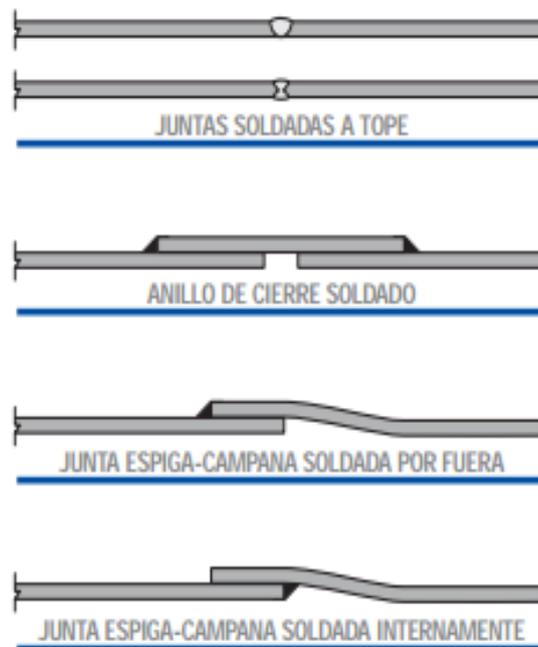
Juntas por soldadura en tuberías de acero
